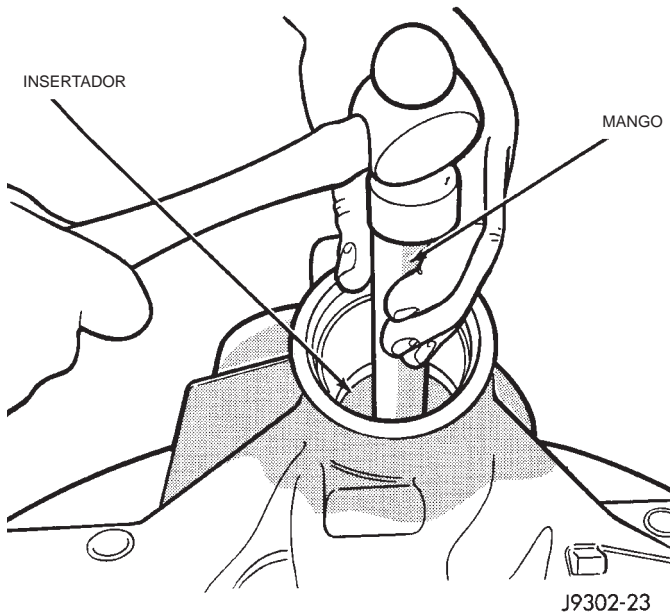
Desmontaje de la cubeta del cojinete trasero
